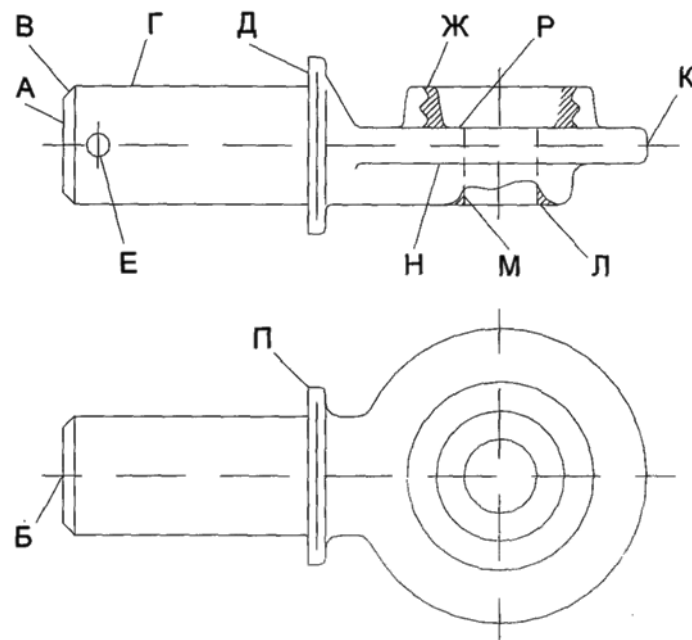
Основні поверхні деталі – опора ПЛН-48.305
